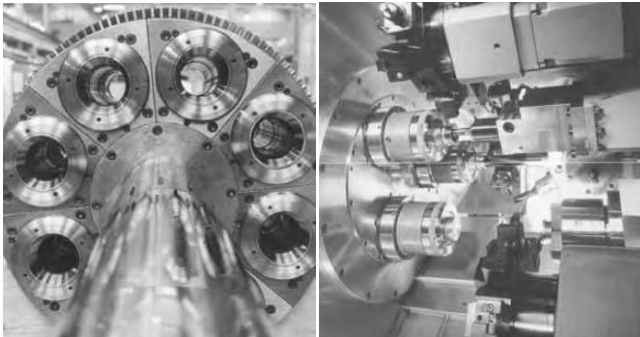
Багатошпindelні токарні верстати фірми DMG: а - шпindelльний барабан;
